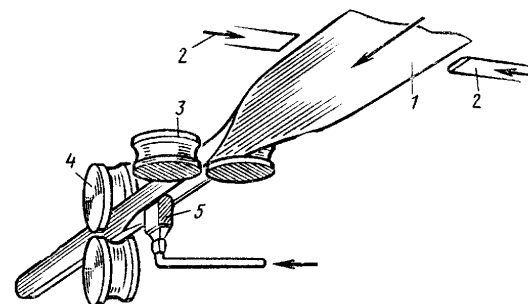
Схема непрерывного процесса печной сварки водогазопроводных труб
